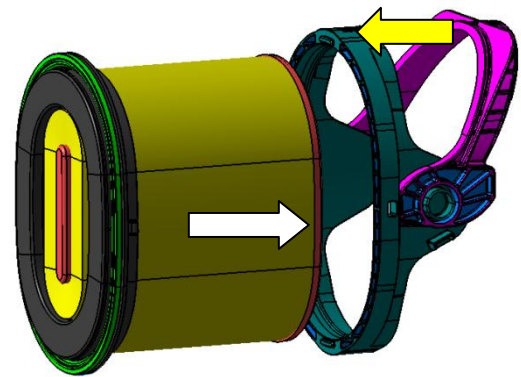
Staffa di serraggio IQORON elemento di dimensioni 10 - 14
